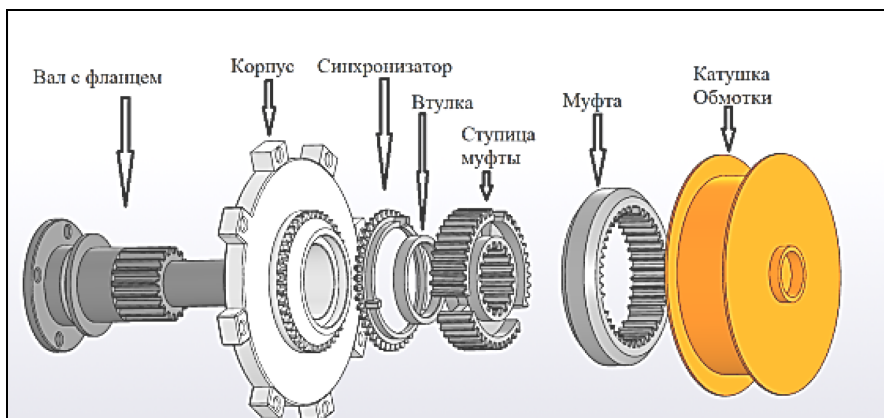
Схема зубчатой муфты разработки автора в ПК «КОМПАС-3D»
